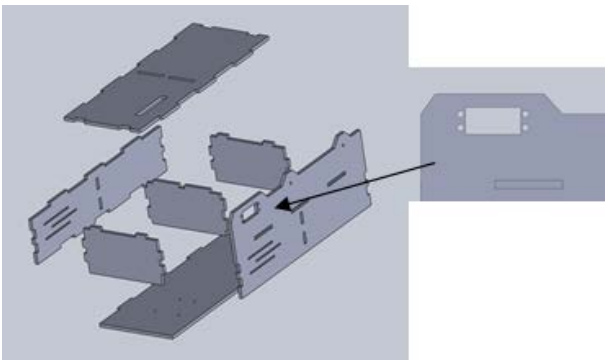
Diseño de la base del mecanismo en 3D usando Solidworks mostrando el detalle de el acoplamiento del servomotor
